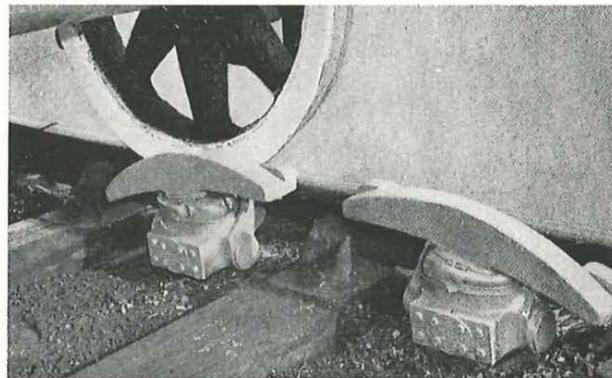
Frein hydraulique pour wagons ou berlines. Vue d'ensemble.
